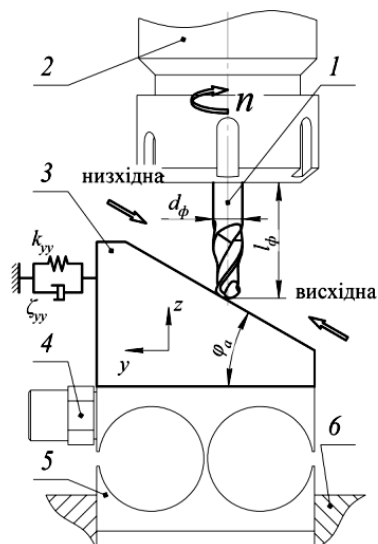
Схема експериментальної установки: 1 – твердосплавна монолітна двозуба сферична кінцева фреза $\varnothing 8$; 2 – цанговий патрон ВТ40; 3 – заготовка з оброблюваною поверхнею, нахиленою під кутом φ_a ; 4 – перетворювач п'єзоелектричний вібровимірювальний моделі ДН-4-М1; 5 – підкладка, піддатлива в напрямку осі y ; 6 – губки лецят
